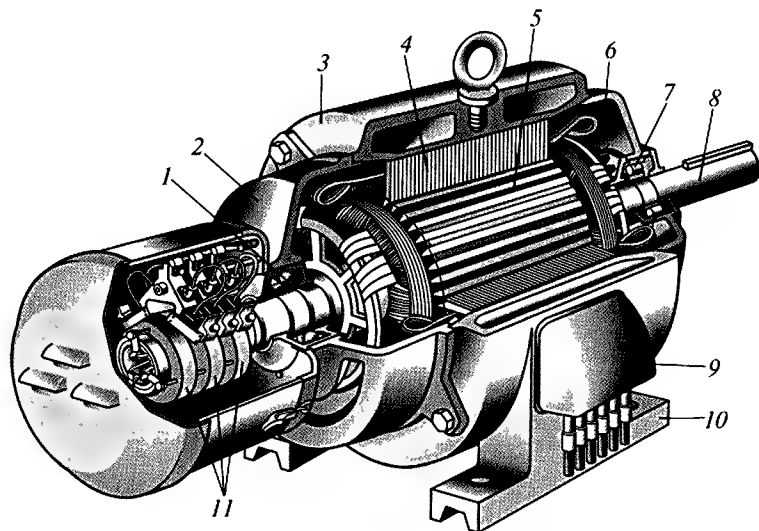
Устройство трехфазного асинхронного двигателя с фазным ротором: *1, 7* — подшипники; *2, 6* — подшипниковые щиты; *3* — корпус; *4* — сердечник статора с обмоткой; *5* — сердечник ротора; *8* — вал; *9* — коробка выводов; *10* — опорные лапы; *11* — контактные кольца
